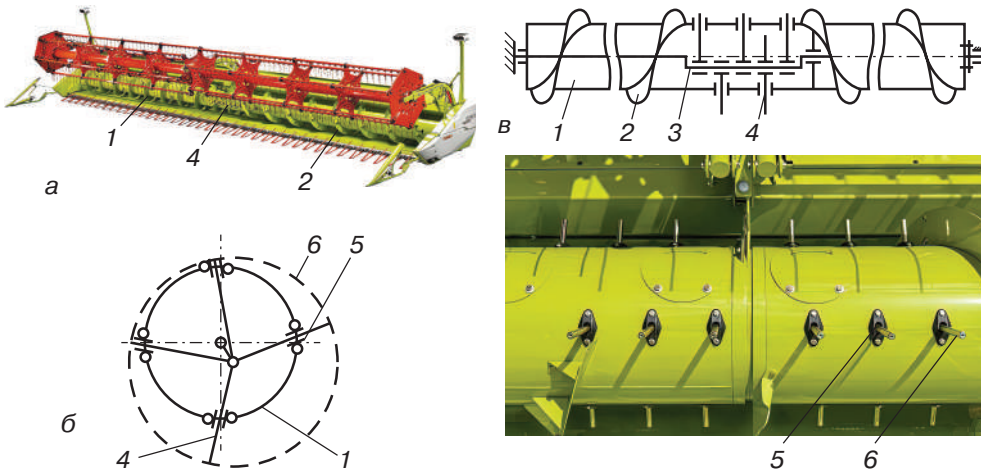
Загальний вигляд шнека жатки (а), його принципова схема (б) та будова пальцевого механізму (в): 1 — корпус шнека; 2 — спіральні витки; 3 — колінчаста вісь; 4 — палець; 5 — вічка; 6 — траєкторія руху пальців
